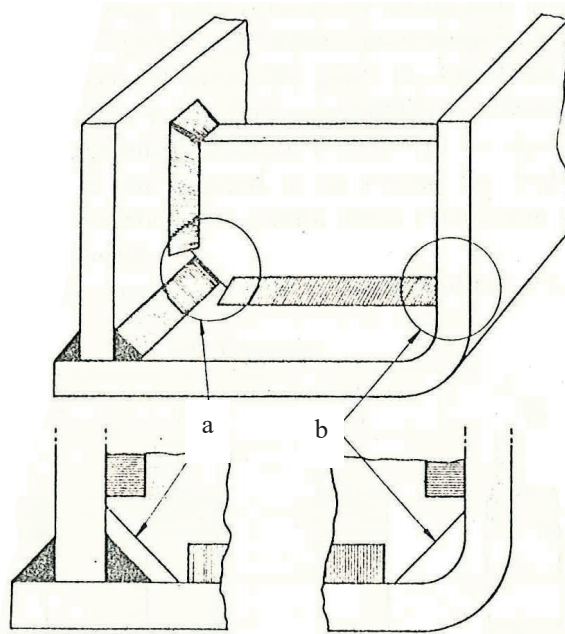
Folgas entre superfícies soldadas
